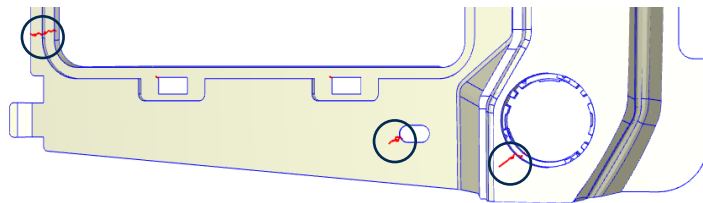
Apresentação de linhas de soldadura no Moldex3D®
